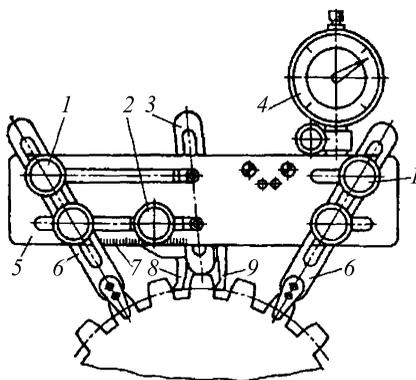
Шагомер для измерения шага зубчатого колеса
